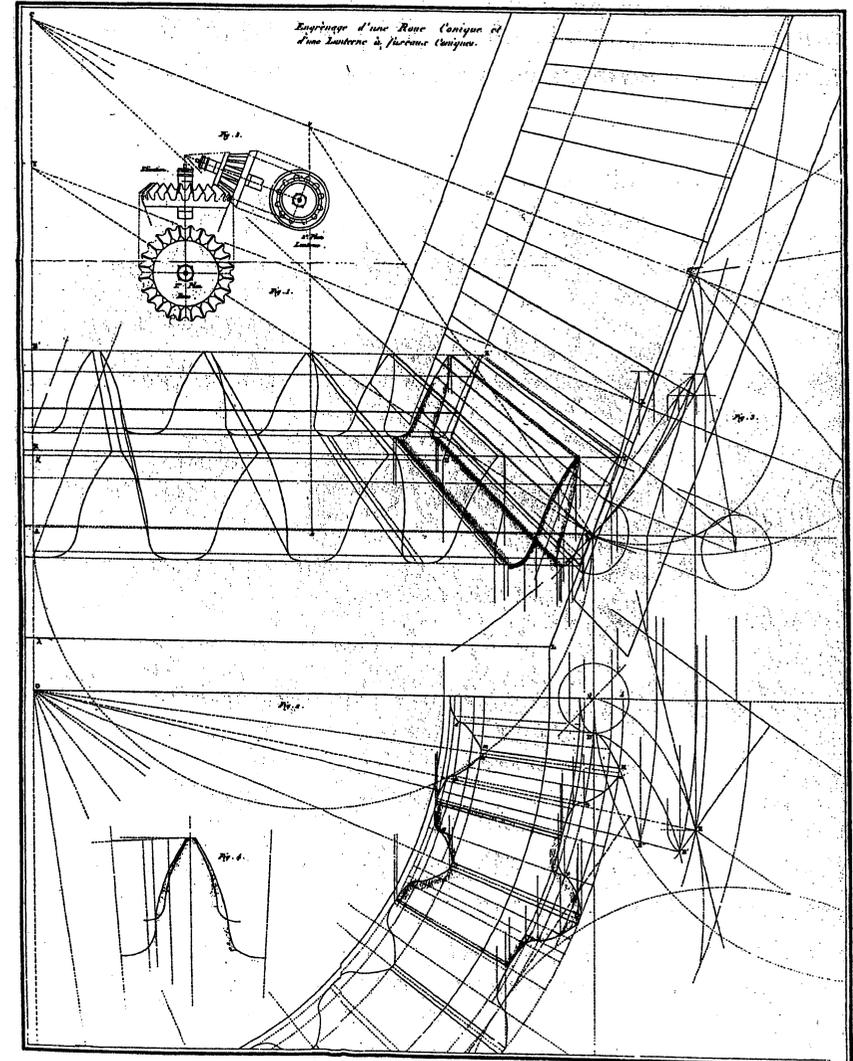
/2: Präzisionszeichnung für eine Kegelradverzahnung (um 1811)
